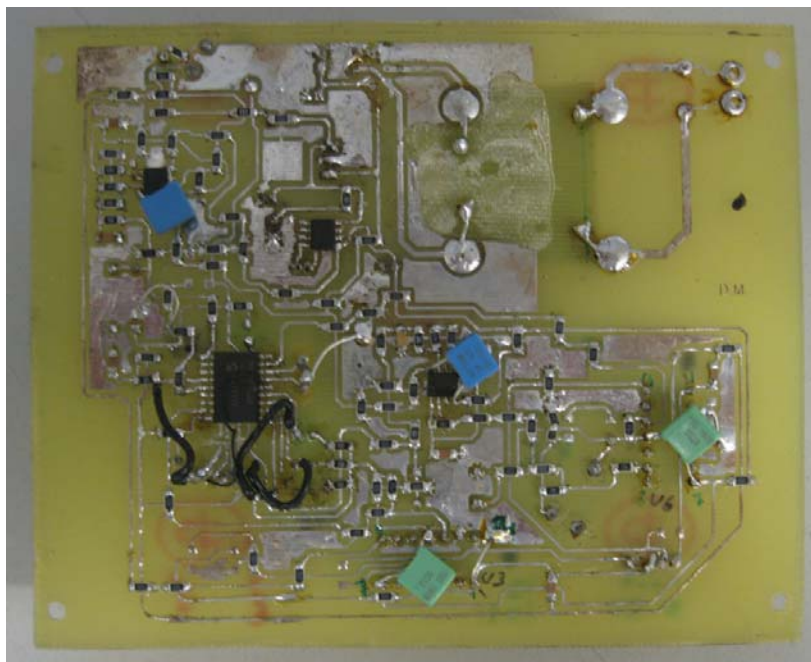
Versió 1 de la PCB amb les modificacions realitzades.
